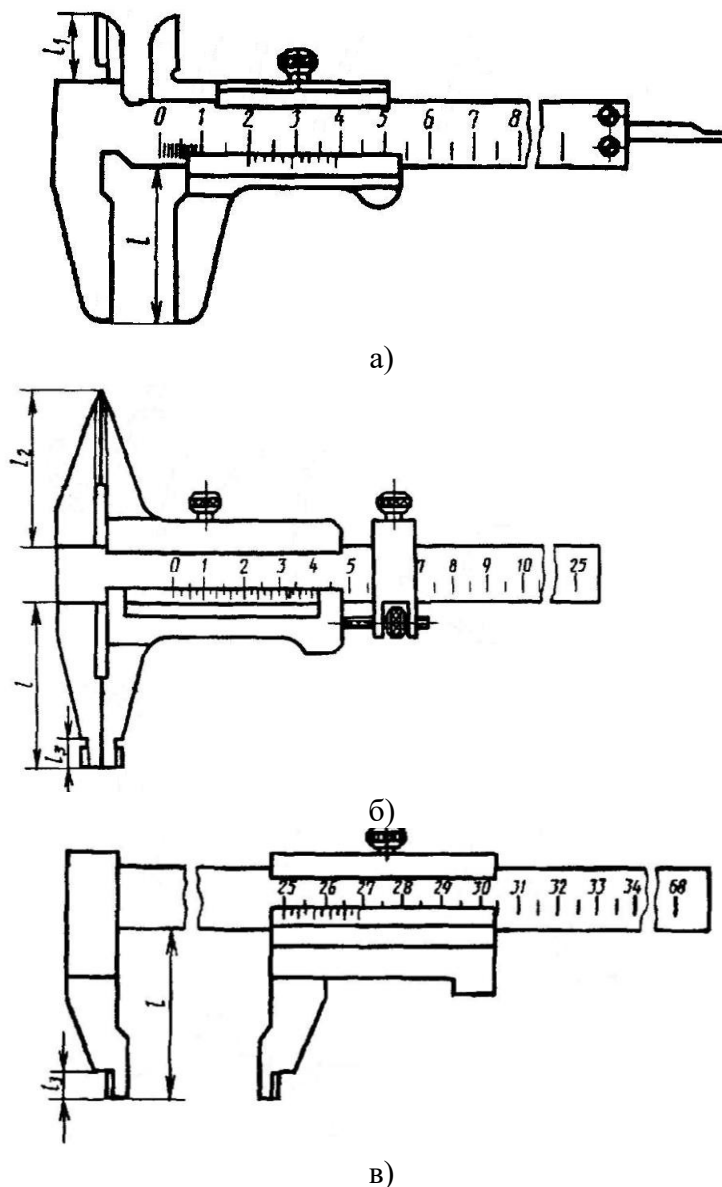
Схемы обозначения губок штангенциркулей типов:
